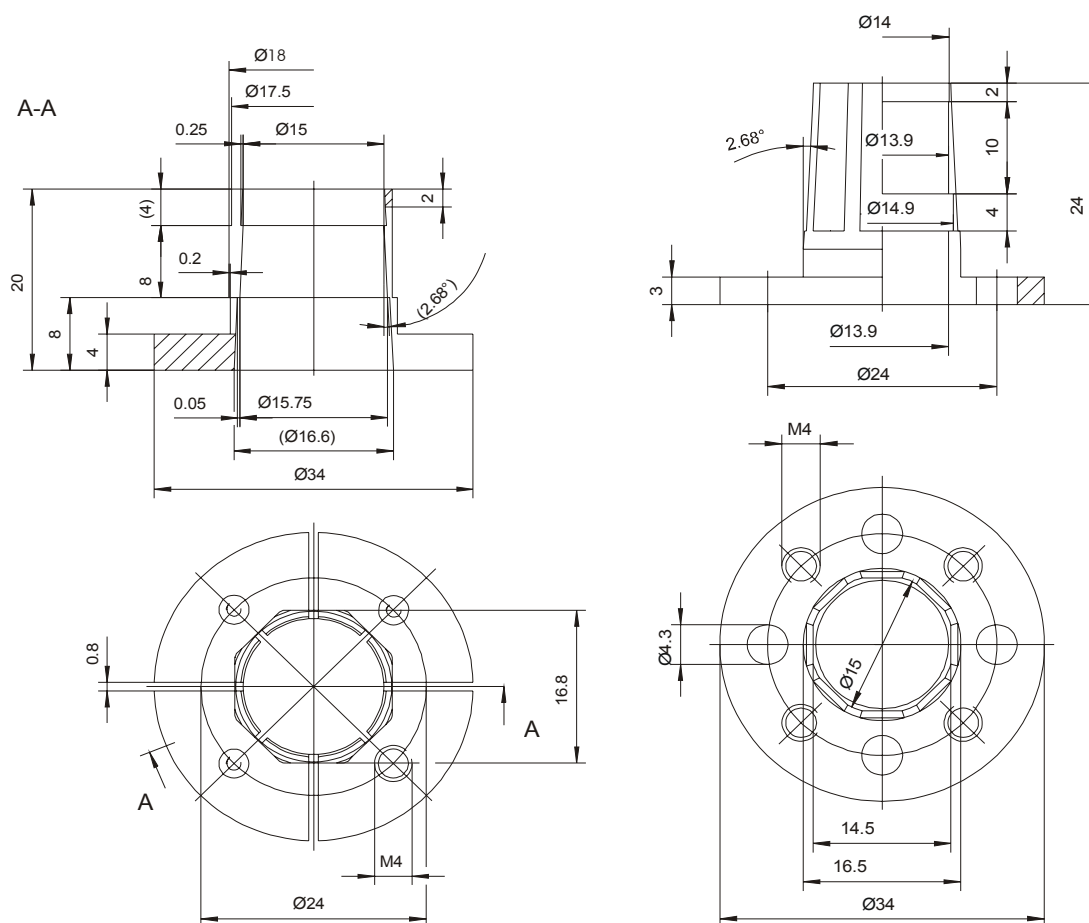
Technische Zeichnung von Außen- und Innenteil des Sensors in seiner endgültigen Ausführungsform
